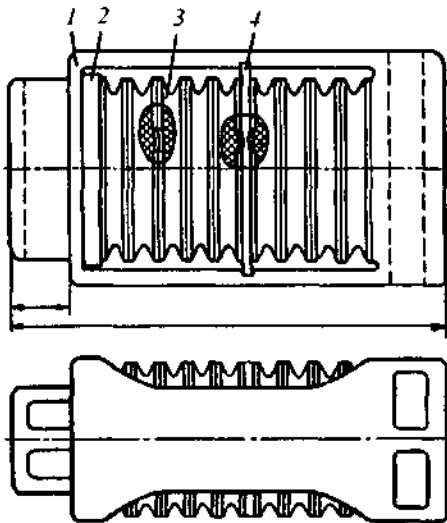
Резинометаллический поглощающий аппарат автосцепки пассажирских вагонов: 1 — корпус; 2 — нажимная плата; 3 — резинометаллические элементы; 4 — промежуточная плита
